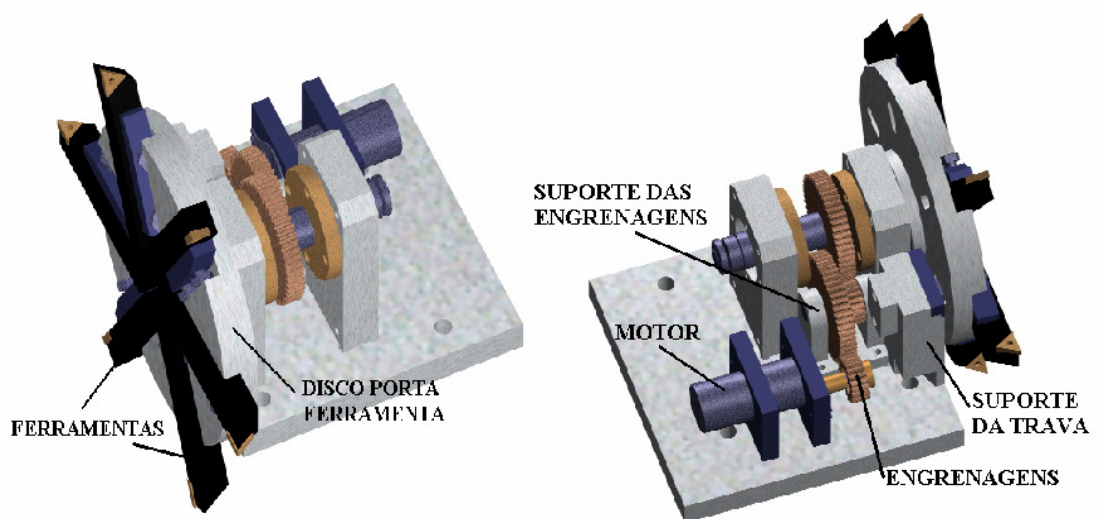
Montagem do disco, das engrenagens, dos suportes e do motor
